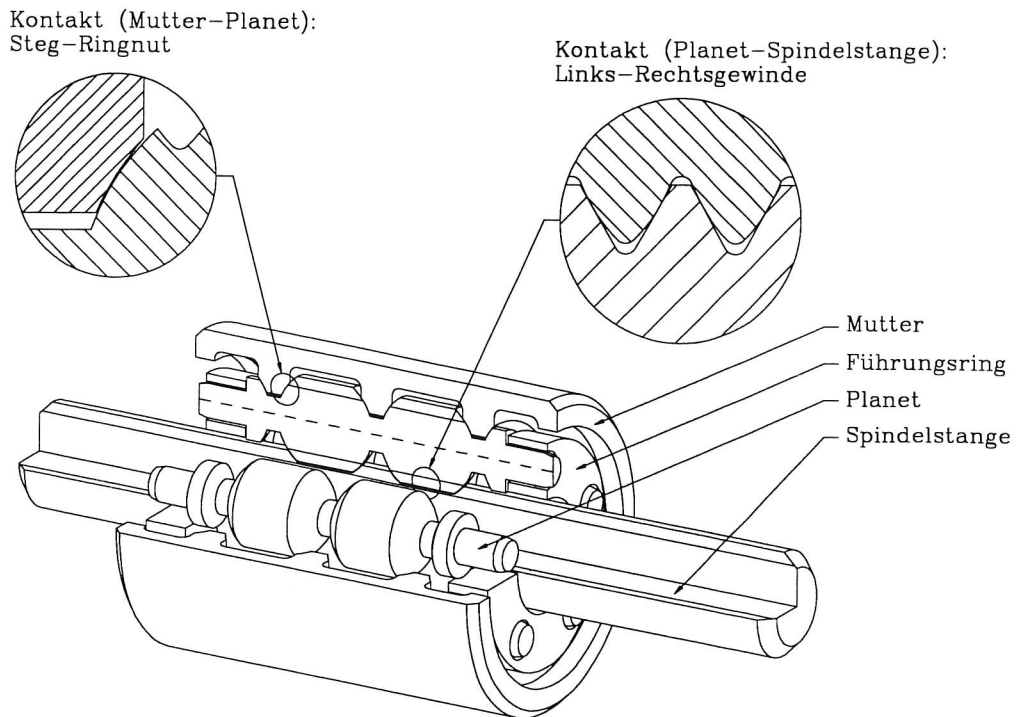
Ausführung der Planeten-Wälz-Gewindespindel (PWG)
